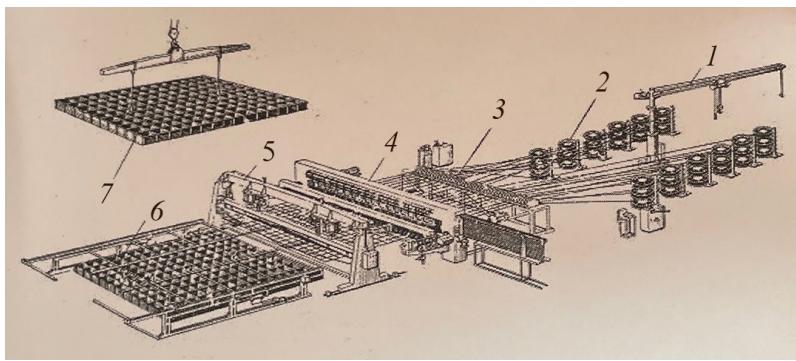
Общий вид автоматизированной линии 7934/1 с бухтодержателями СМЖ-58А: 1 – консольный кран; 2 – бухтодержатель; 3 – правильное устройство; 4 – сварочная машина; 5 – ножницы; 6 – пакетировщик; 7 – транспортируемый пакет сеток
